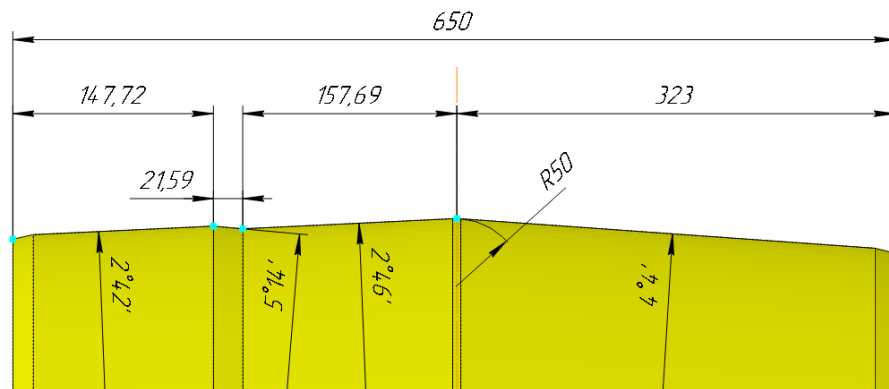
Бочка валка прошивного стана ТПА 220 после реконструкции. 3D модель
